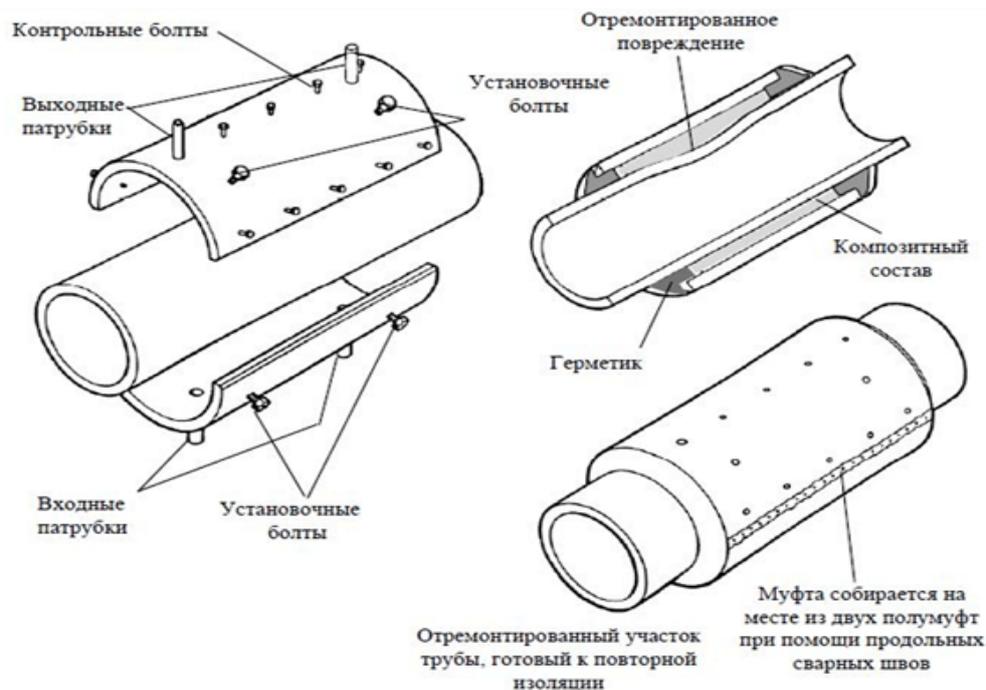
Ремонтная муфта со сварным соединением полумуфт
